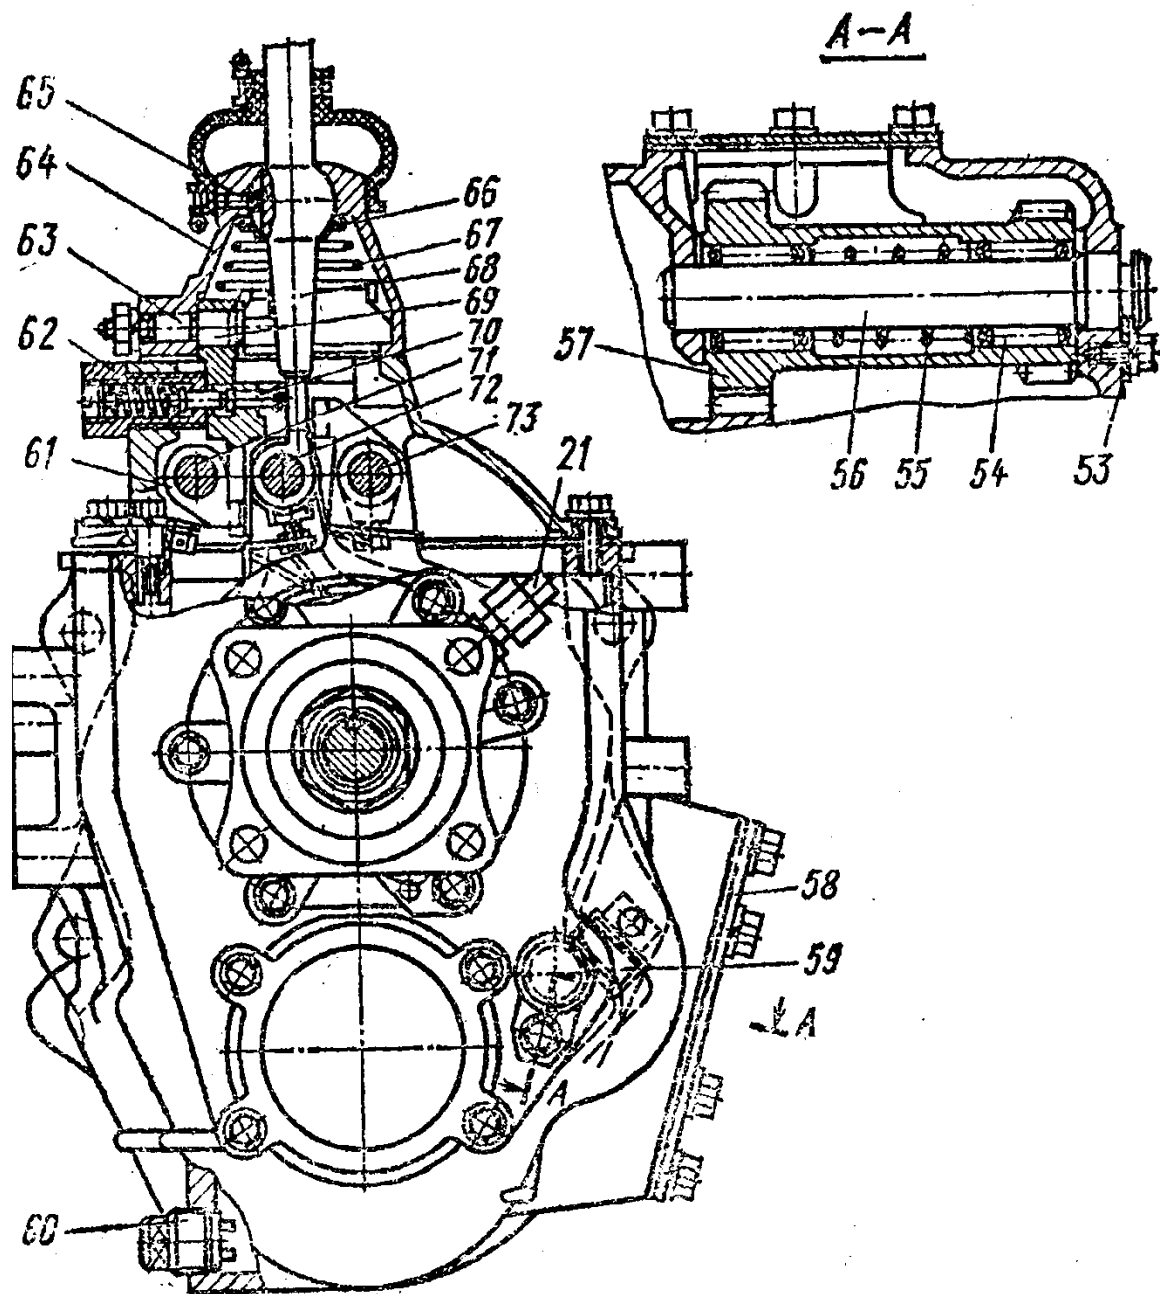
Коробка передач ЗІЛ-130 (поперечний розріз)
